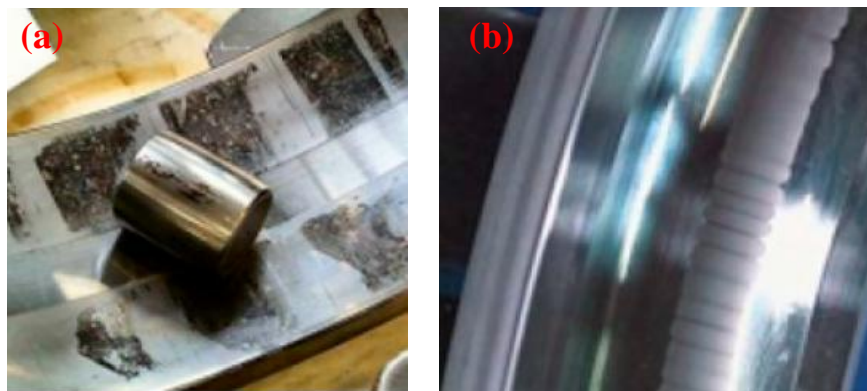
(a) Corrosion par humidité (b) corrosion par frottement [44]
